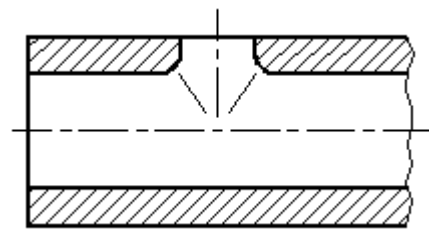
Образец оформления линий плавного перехода поверхностей.
